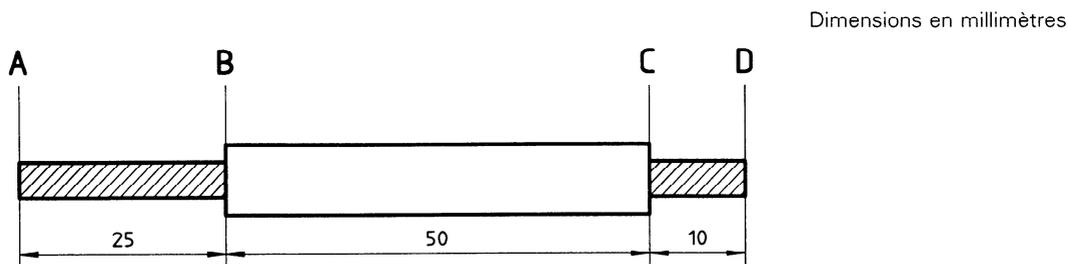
Échantillon d'essai d'adhérence de la couche d'isolation sur le conducteur
